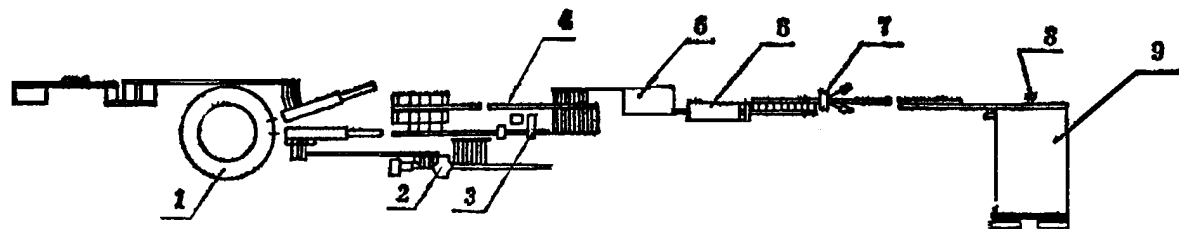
日本山阳特钢三辊轧管机组平面布置图
